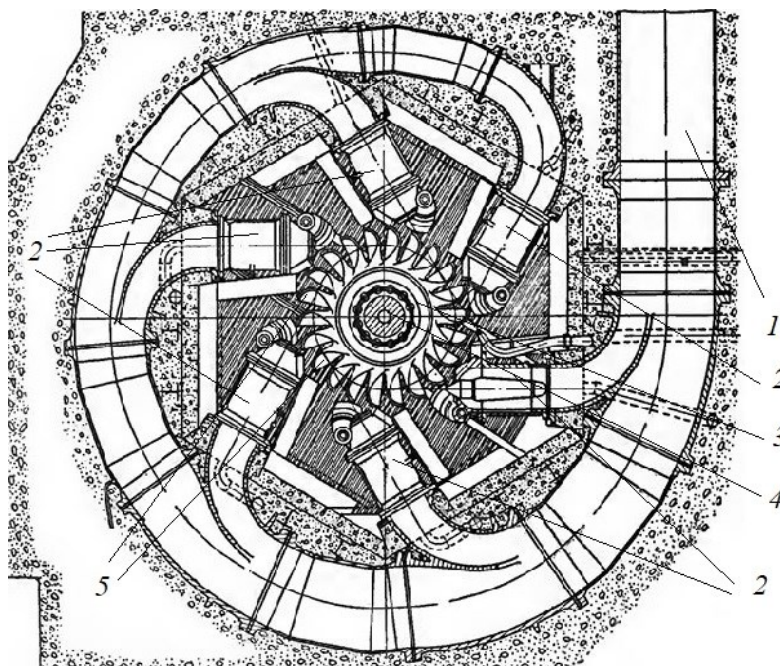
Схема ковшовой гидротурбины: 1 – подводящий трубопровод; 2 – сопло; 3 – рабочее колесо; 4 – вал; 5 – рабочие лопатки.
